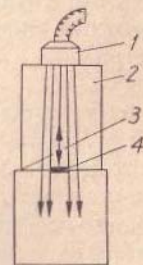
Схема прозвучивания сварного стыка инструмента.
